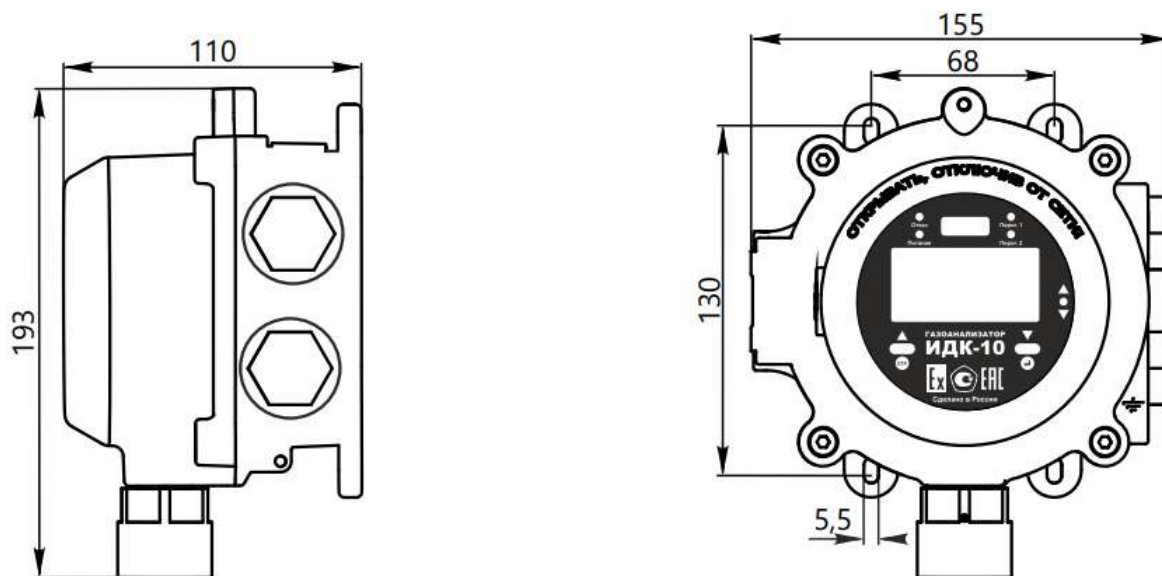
Габаритный чертеж ИДК-10-01 с ОСЗВ
